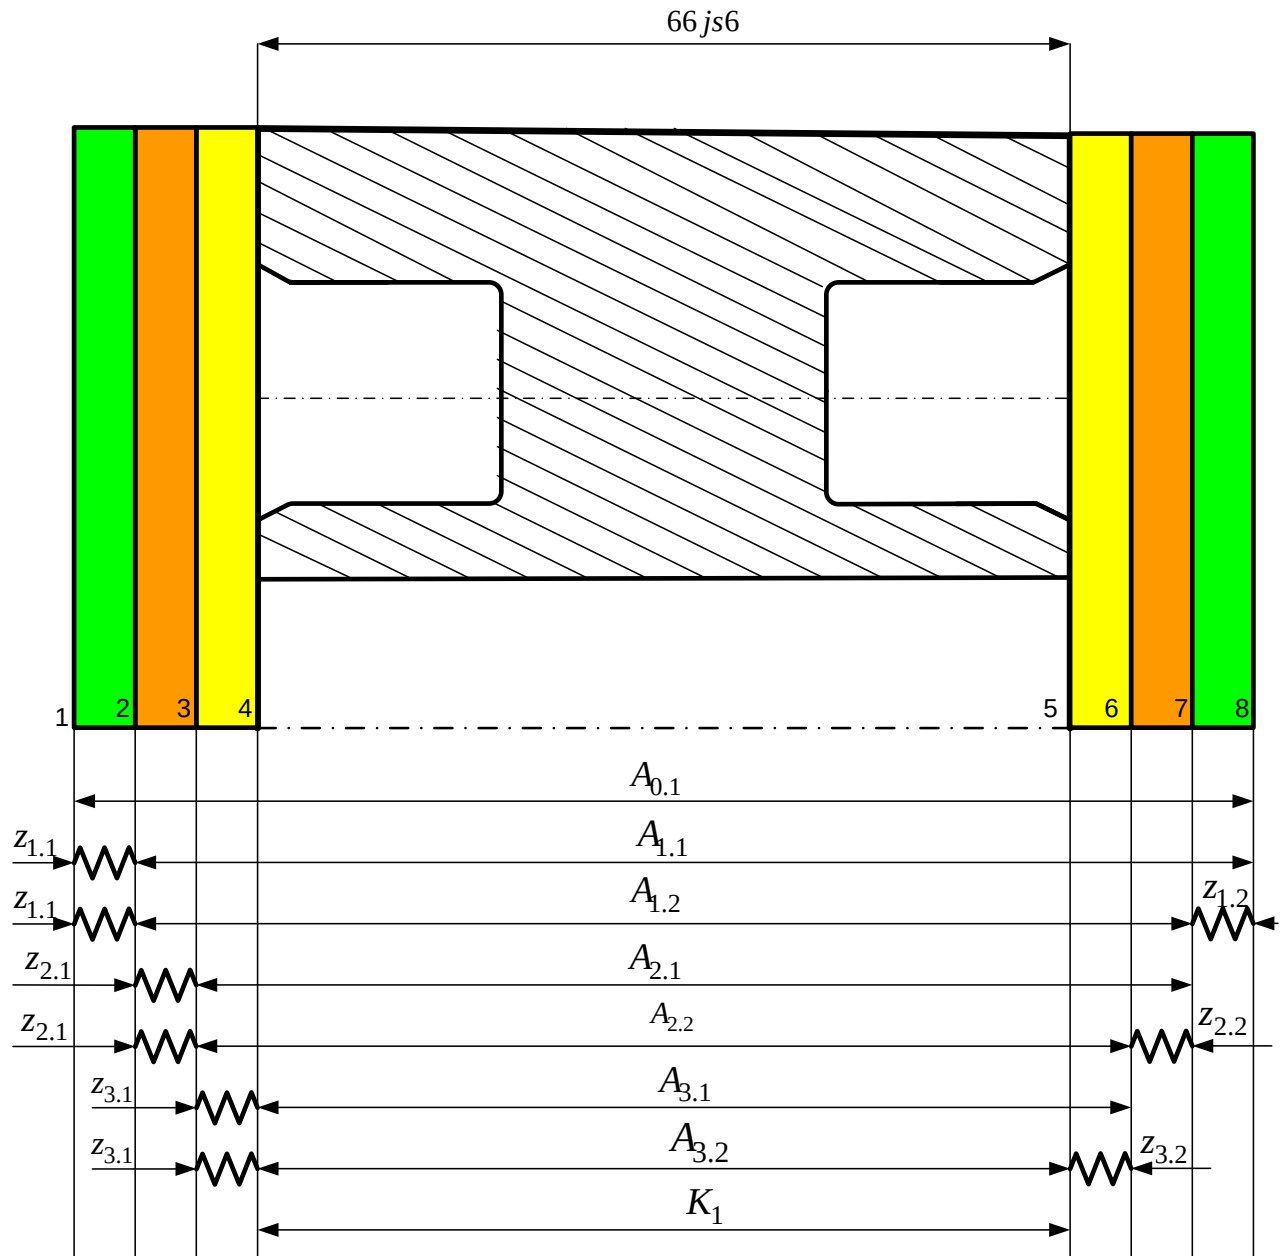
Размерная схема ТП механической обработки зубчатого колеса (осевое направление)
